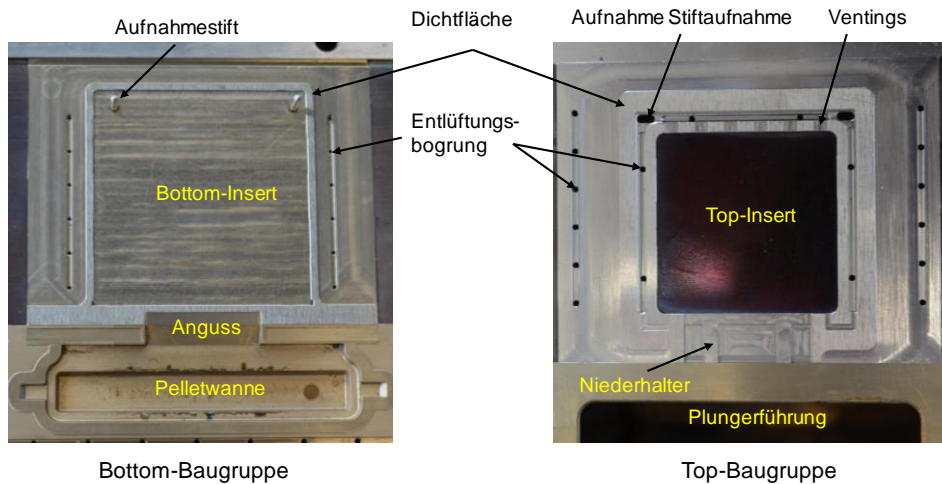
Gefertigte, zusammengebaute und im Werkzeug integrierte Bottom- sowie Top-Baugruppe.
